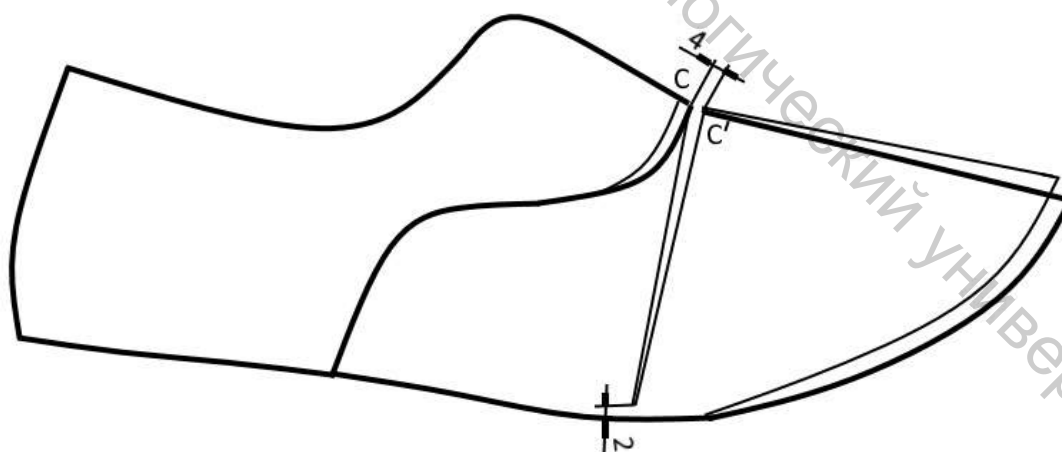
Корректировка конструктивной основы подкладки
